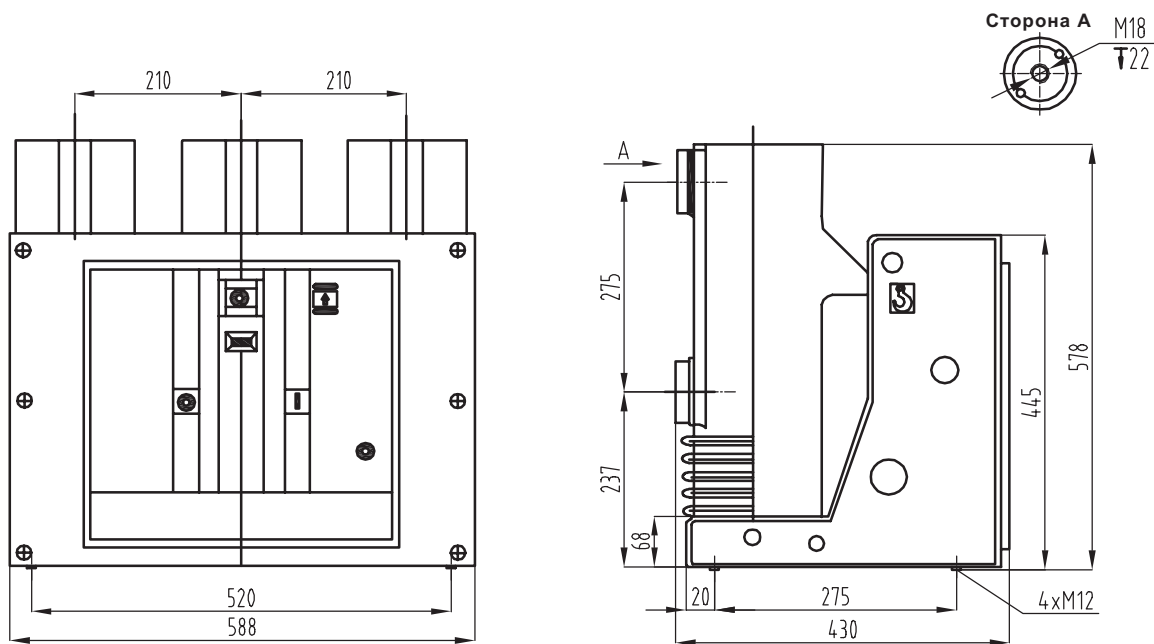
Габаритный размер выключателя ВВ стационарного исполнения для ячейки шириной 800 мм
